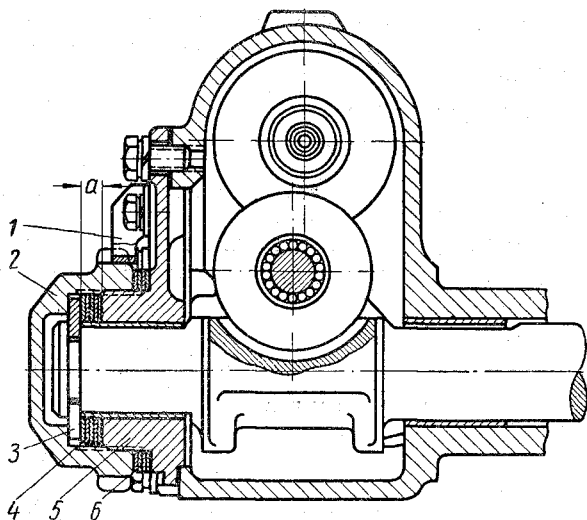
Регулировка зацепления червячной пары рулевого механизма:
